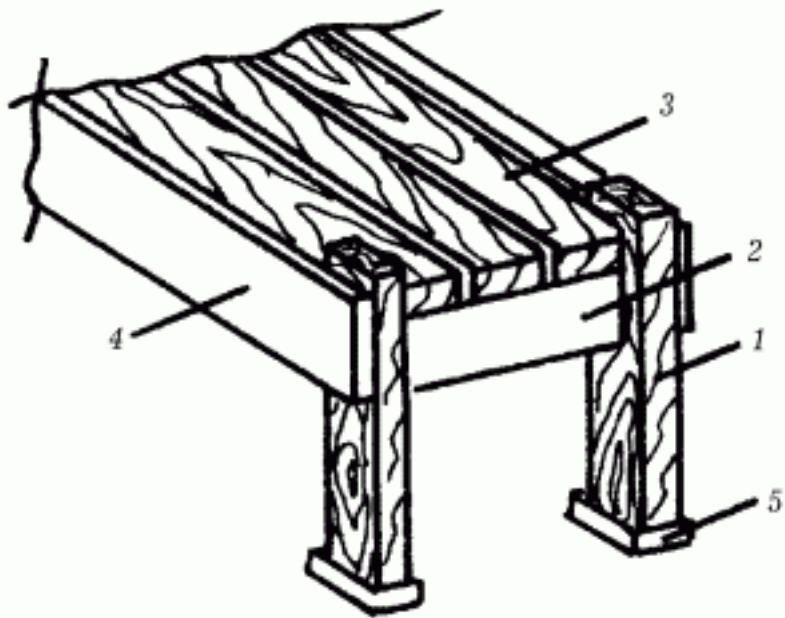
Скамейка для бани: 1 – стойка; 2 – опорный брусок; 3 – доски; 4 – рамный брусок; 5 – резиновая подножка.
